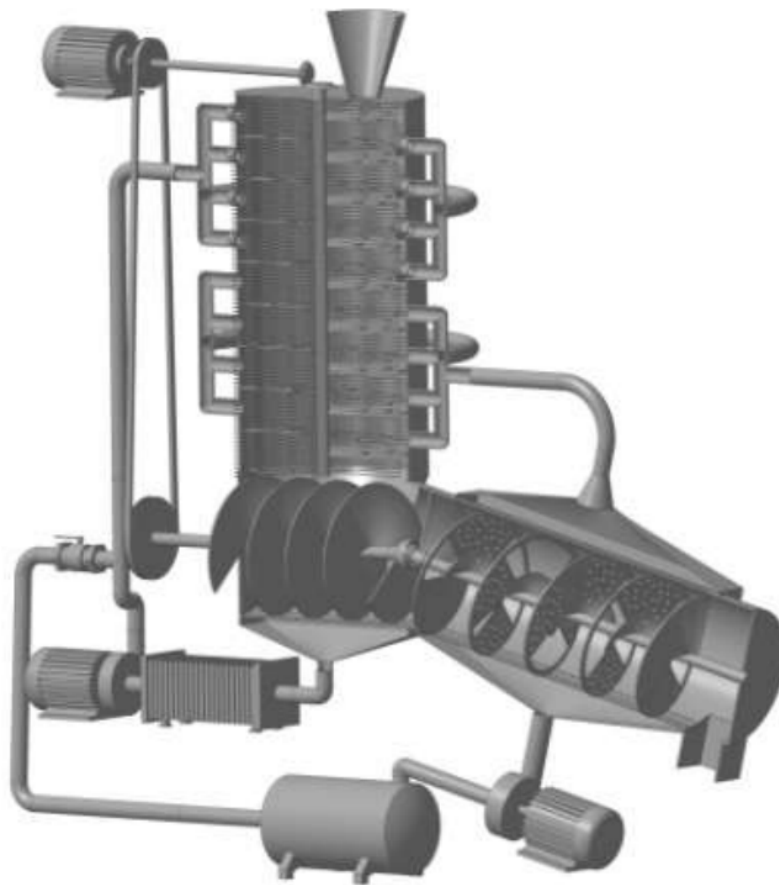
Апарат для гідротермічної обробки олійних культур: 1 - завантажувальна лійка, 2 - камера мийки, 3 - зубчаста передача, 4 - електродвигун, 5 – пасова передача, 6 - форсунки, 7 - багаторядні щітки, 8 - патрубки, 9 – транспортуючий шнек, 11 - шарнір, 12, 15 - конфузори, 13 - фільтр, 14 - трубопровід, 16 - паропровід, 17 - дифузор, 18 - комбінований шнек, 20 - вентилятор, 22 - парогенератор, 23 - спиралеподібна стрічка, 24 - виступи, 25 - насос, 26 - сегментний виріз, 27 - шків, 28 - камера обсмаження, 29 – горизонтальна циліндрична камера відокремлення води від сировини
